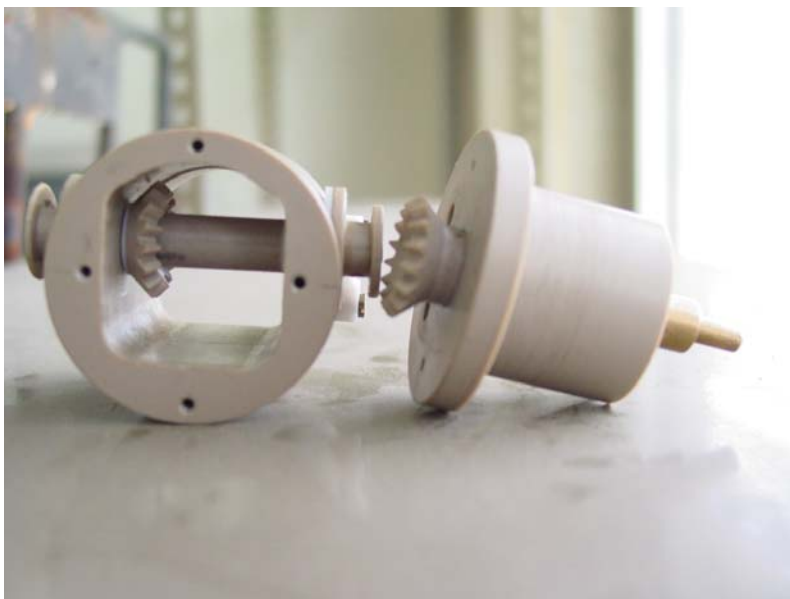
Pormenor do interior do dispositivo, montagem das engrenagens que eram fixadas aos eixos por intermédio de veios de latão. As duas parte principais do dispositivo, o corpo da sonda que basicamente servia de suporte ao eixo horizontal e às amarras, e a bainha do eixo vertical, à esquerda.
